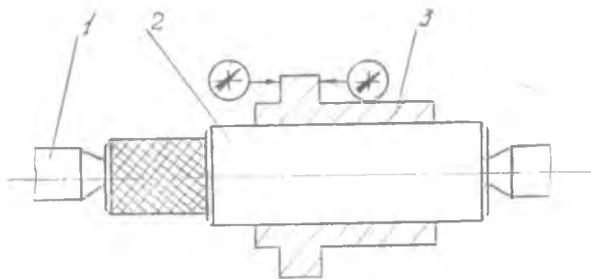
Схема контроля торцевого биения. 1 — центр; 2 — оправка; 3 — проверяемая деталь
